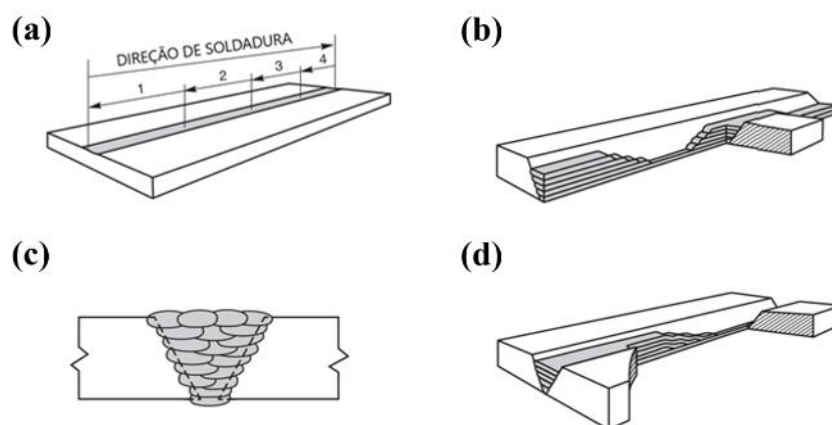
Sequências de soldadura utilizadas para reduzir tensões residuais e distorções. Adaptado de [23]
